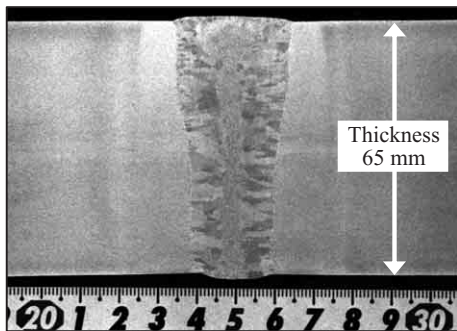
EGW 溶接の断面観察例 (板厚 : 65 mm)
